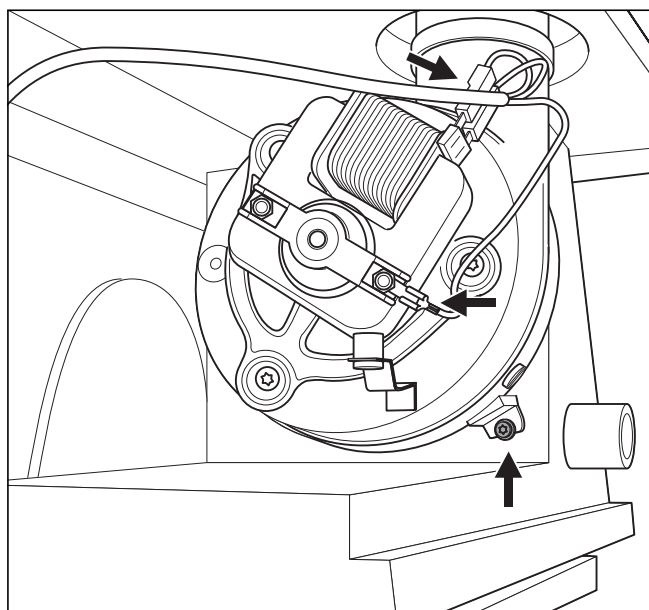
Desmontaje del ventilador tipo 11-4/O y 14-4/O
